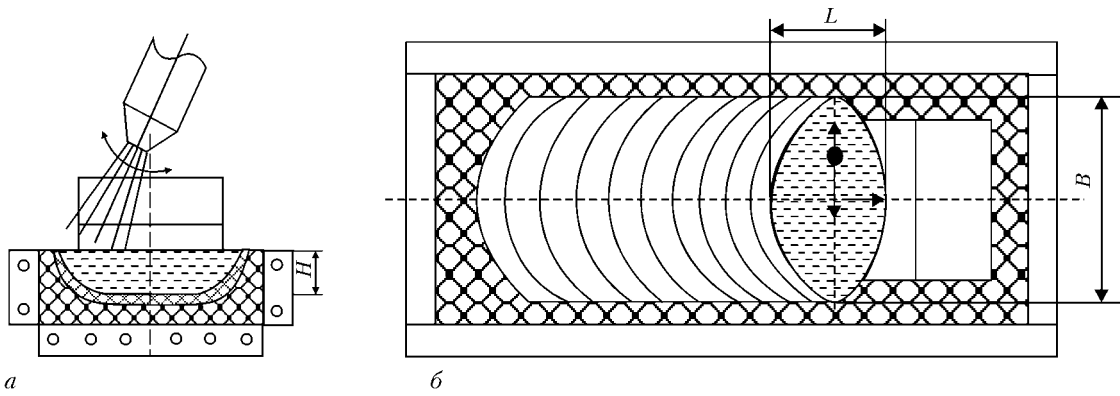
Схема переплава шихты с донной и боковой изоляцией кристаллизатора дисперсной подложкой: *a* — вид со стороны узкой грани кристаллизатора; *б* — вид сверху; *H*, *L*, *B* — соответственно глубина, длина и ширина металлической ванны
